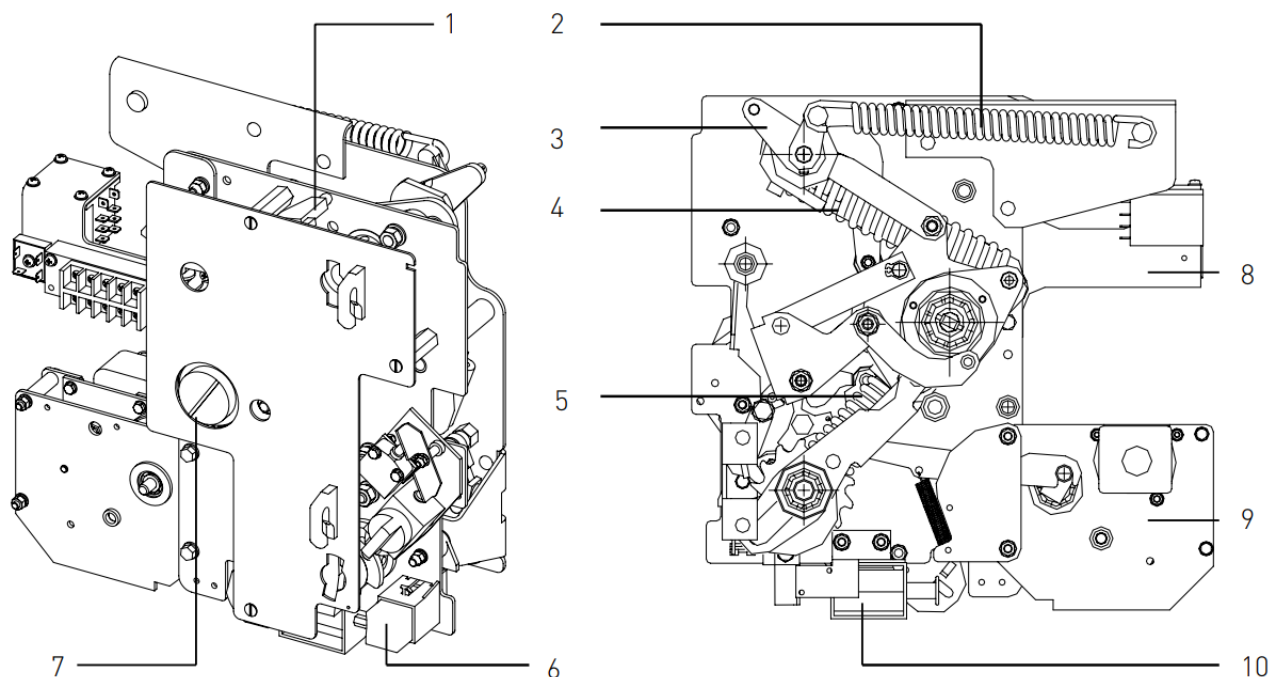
Конструкция привода выключателя нагрузки FLN36-12D
